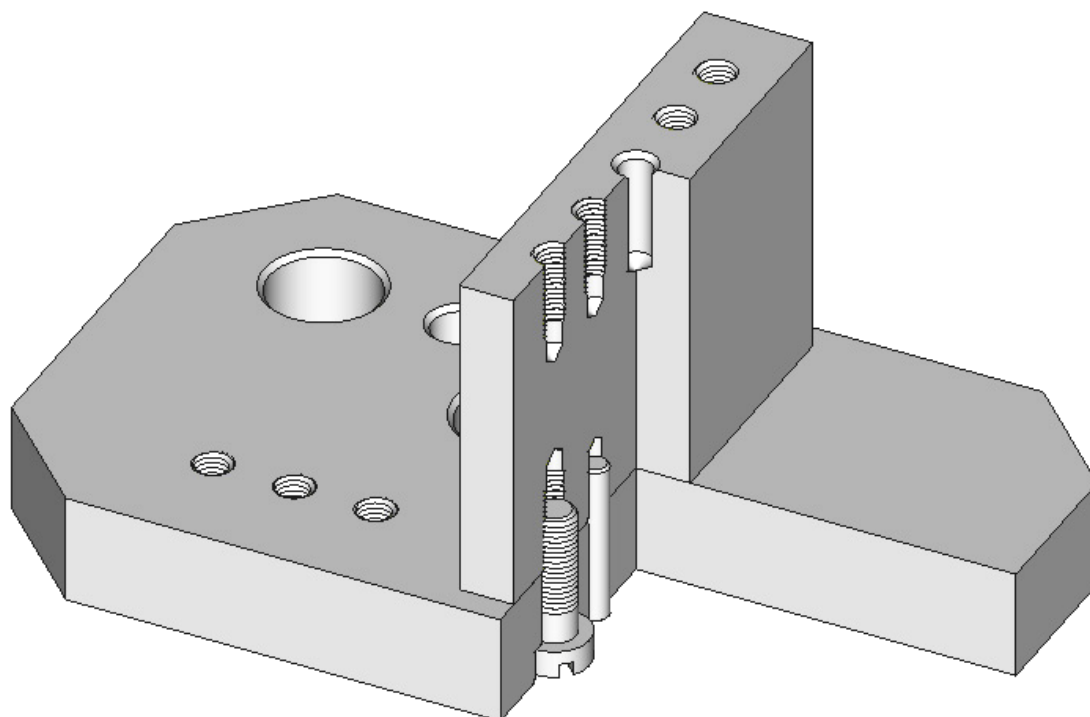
Нижнее крепление корпуса к основанию: конструкция «Тавр»
